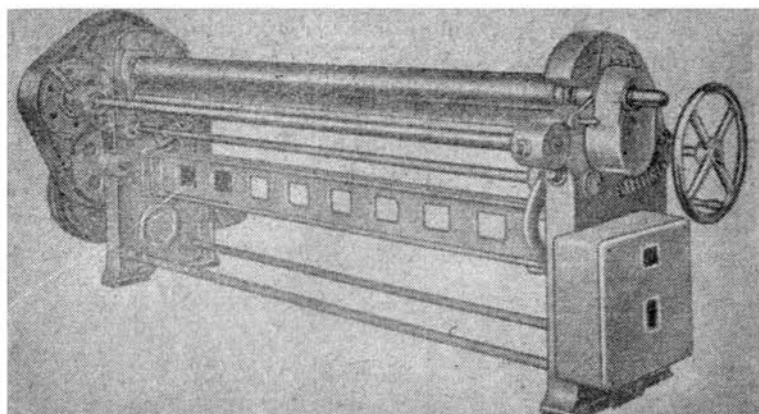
Листогибочный трехвалковый станок с механическим приводом
